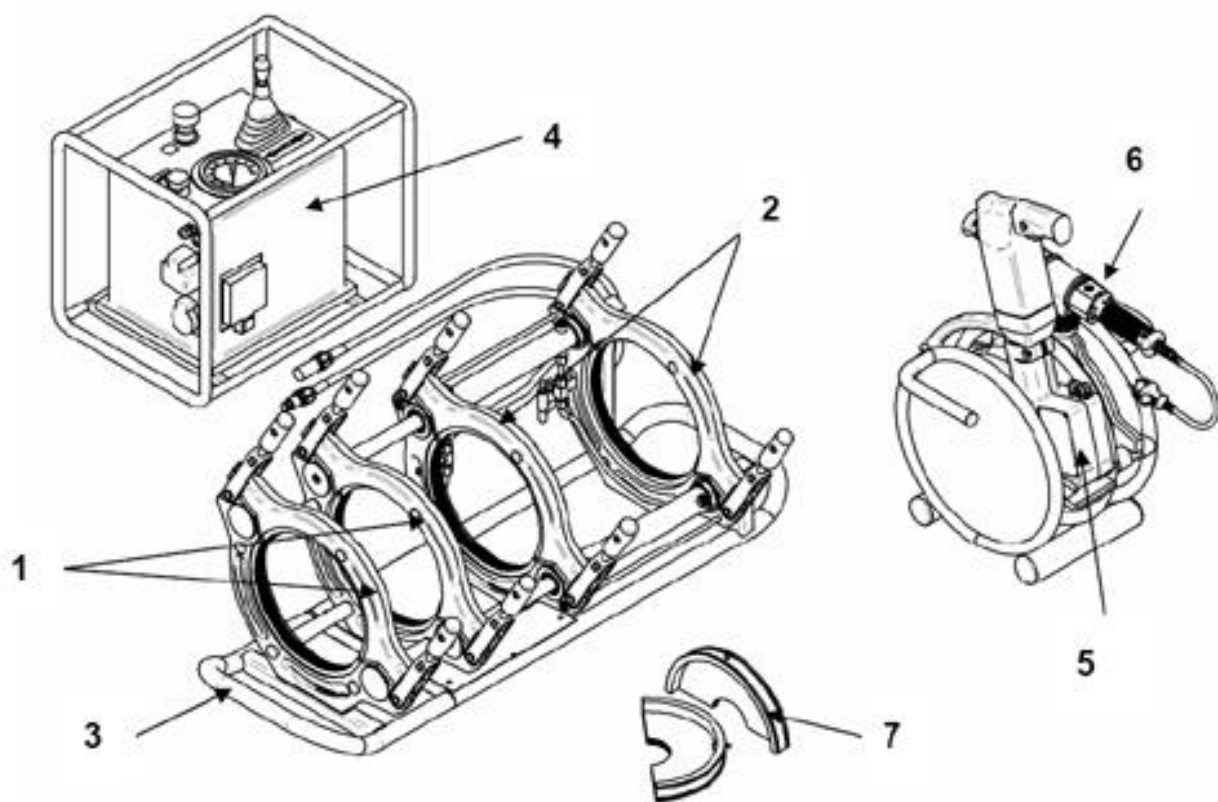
«Состав оборудования с гидравлическим приводом для стыковой сварки
